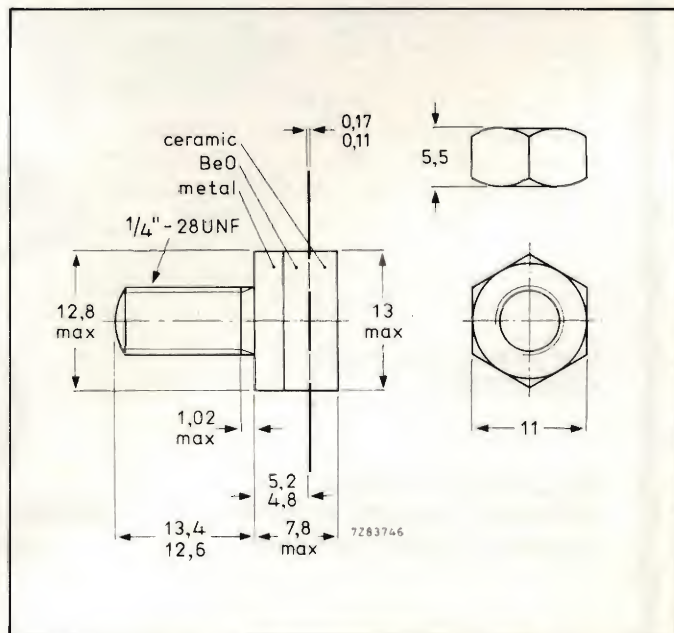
Dimensioni d'ingombro e collegamenti agli elettrodi nel transistor BLV 33.
